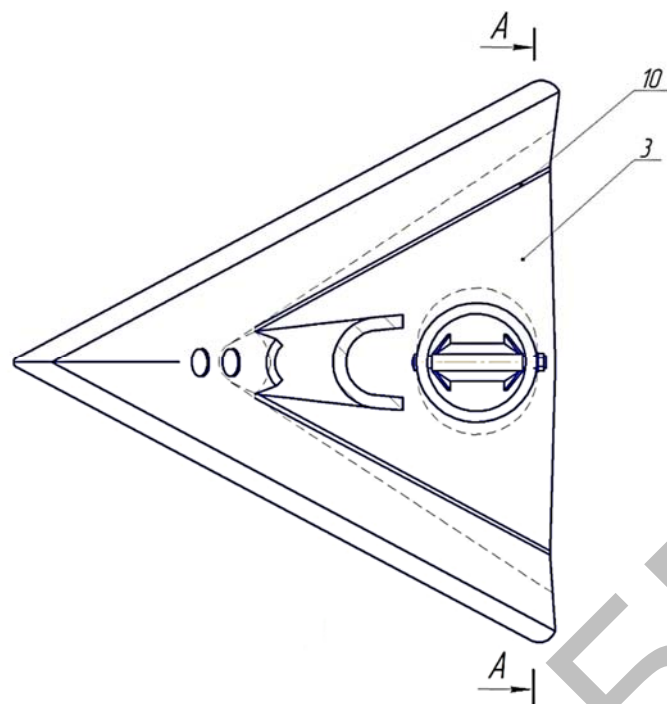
Общий вид сошника для подпочвенно-разбросного посева
